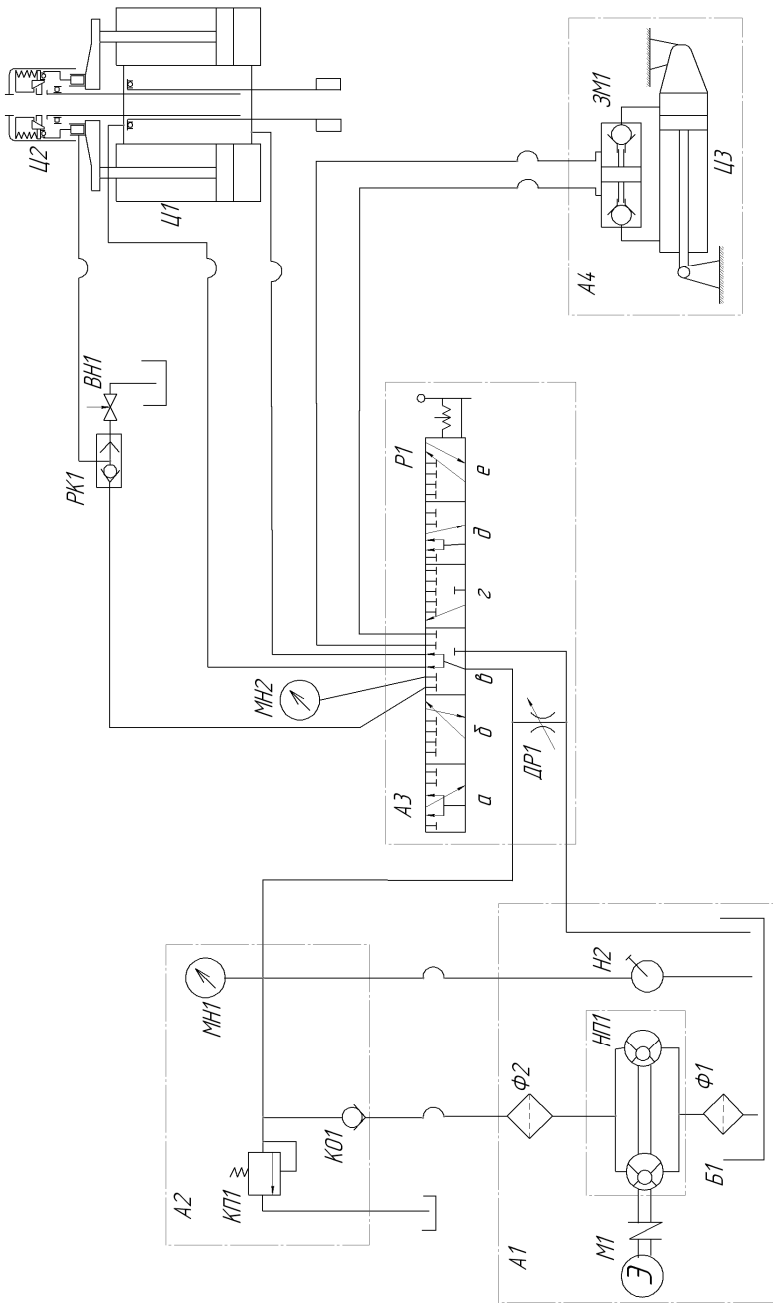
Гидравлическая схема станка SKTO-75
